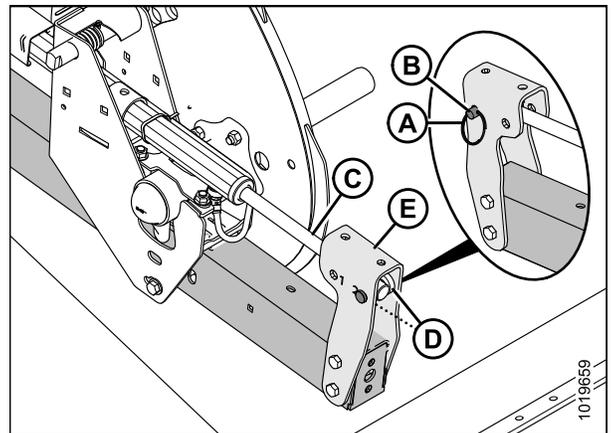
Цилиндр правого рычага мотовила в переднем положении
